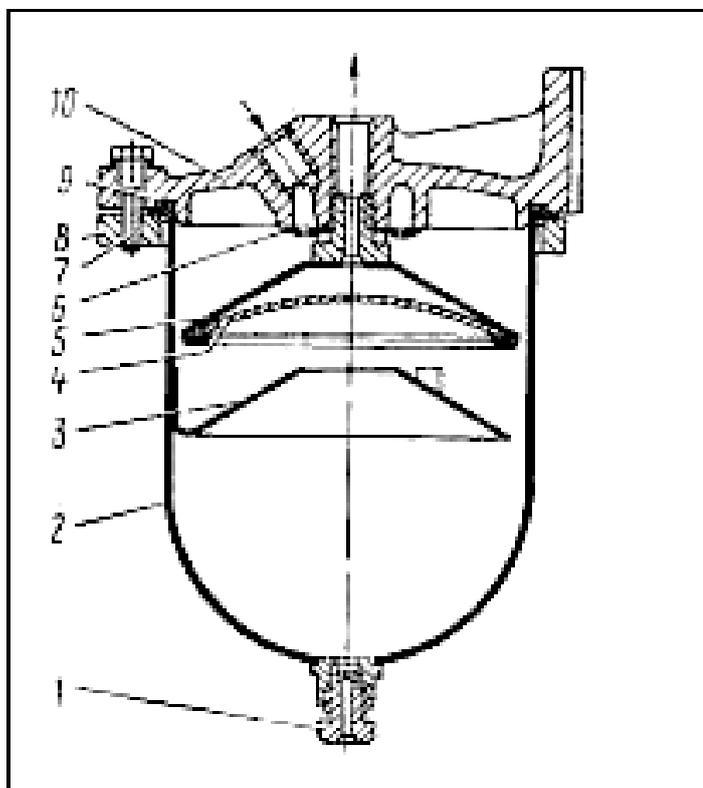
Фильтр грубой очистки топлива КамАЗ-740:
